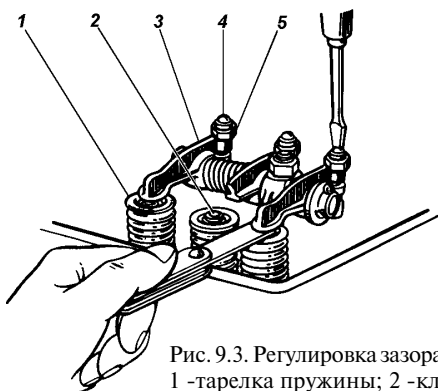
Регулировка зазора между коромыслом и клапаном: 1 -тарелка пружины; 2 -клапан; 3 -коромысло; 4 -регулирующий винт; 5 -контргайка
